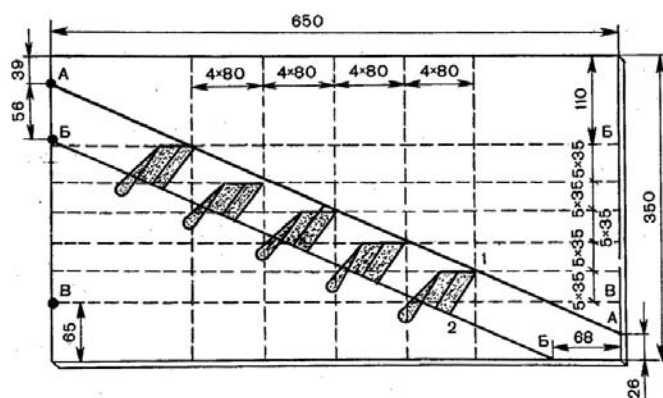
Разметка площадки для проверки установки корпусов плуга (размеры в см): 1 — носок лемеха; 2 — пятка полевой доски
